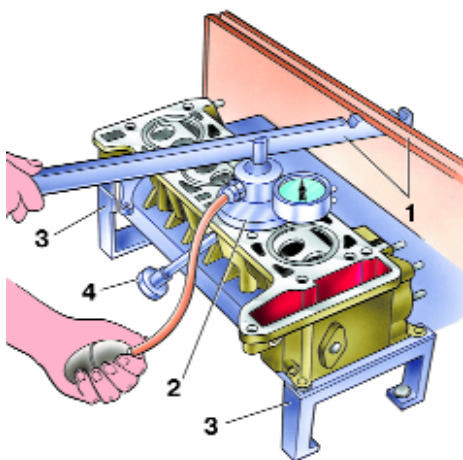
Проверка герметичности клапанов: 1, 2 – приспособления; 3 – подставка; 4 – пробка для отверстий свечей зажигания
